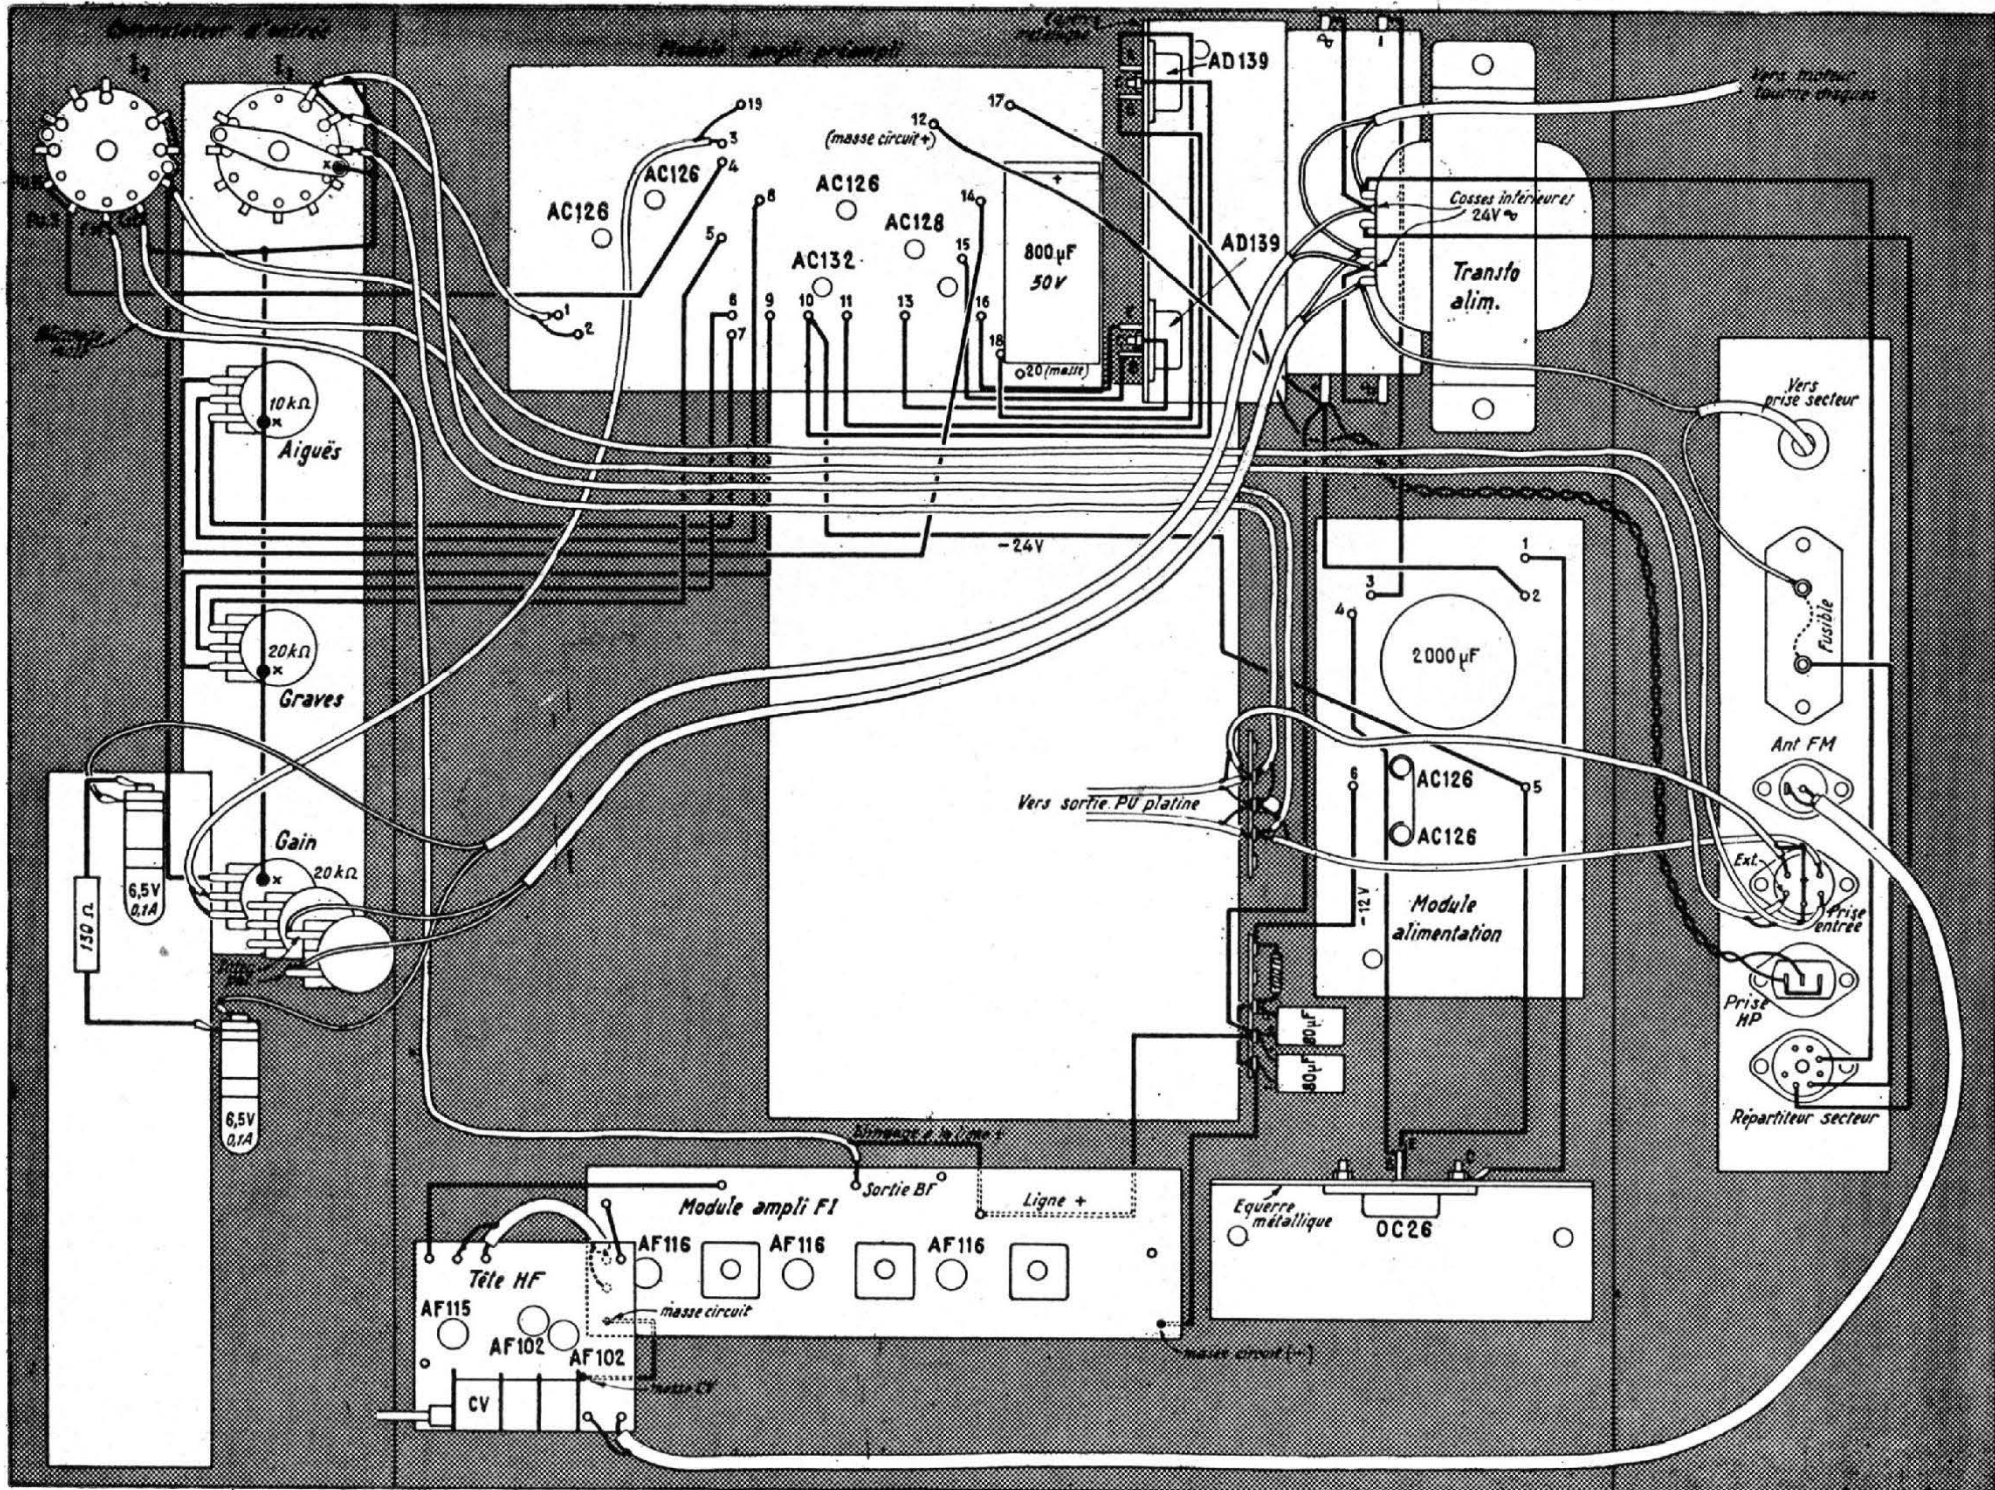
Plan de câblage des différents éléments, fixés au fond du coffret
